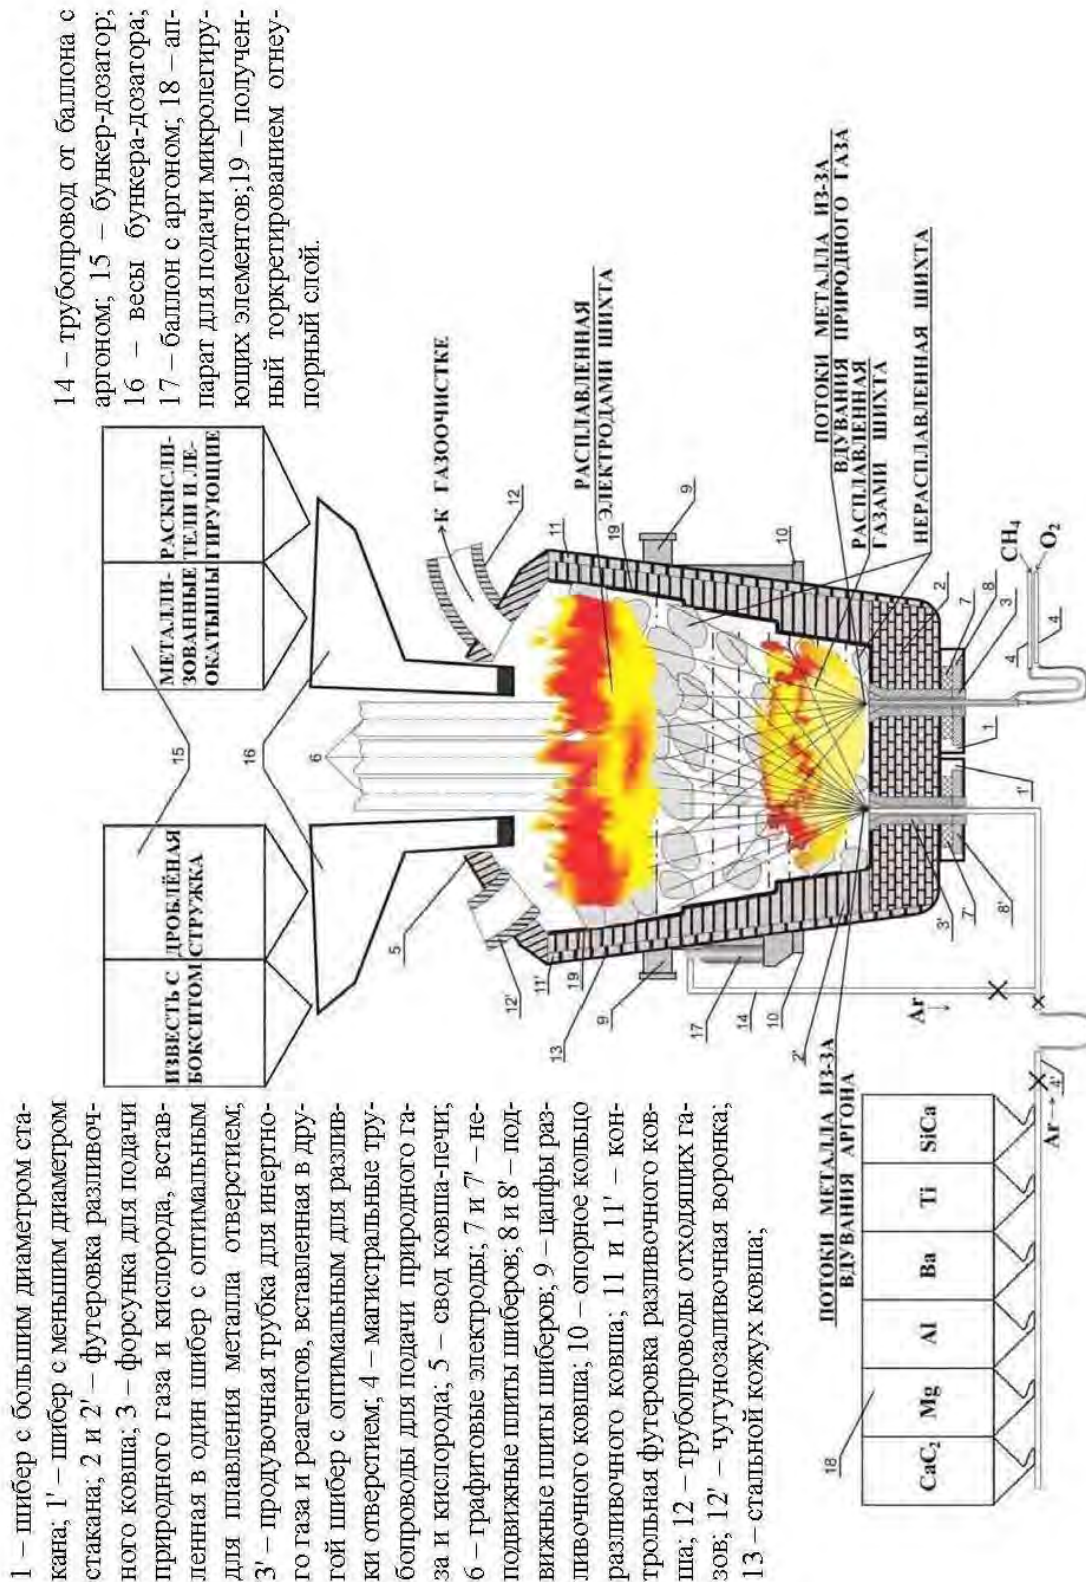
Двухшиберный агрегат для совмещения технологий выплавки, раскисления и обработки стали
